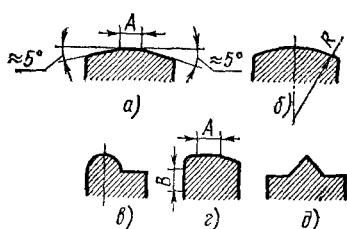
Профили роликов для обкатывания наружных поверхностей:
